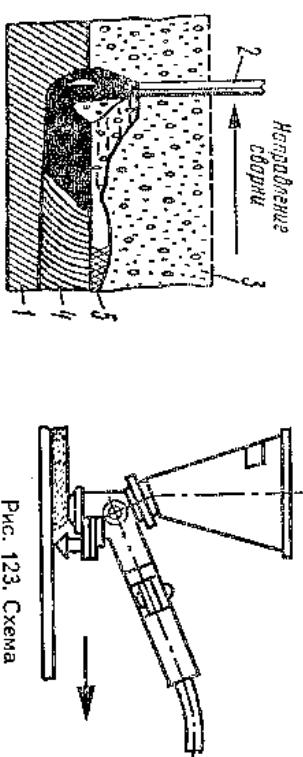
Схема сварки полуавтоматической сварки под флюсом
